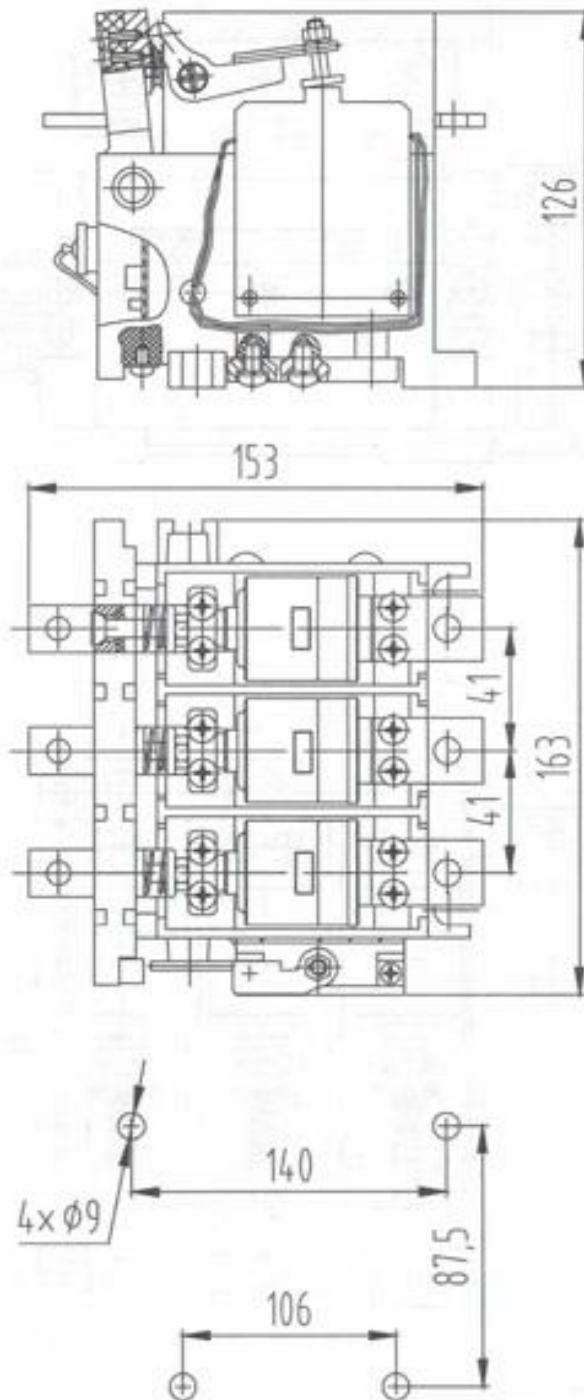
SOSKJ5-80/1140 desenho e dimensional de instalação
